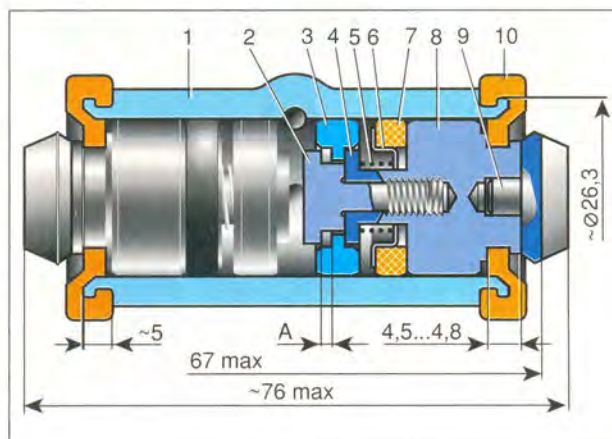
Тормозной цилиндр заднего колеса: 1 – цилиндр; 2 – упорный винт; 3 – упорное разрезное кольцо; 4 – сухари; 5 – пружина; 6 – опорная чашка; 7 – резиновое кольцо; 8 – поршень; 9 – упор колодки; 10 – защитный резиновый колпачок.
